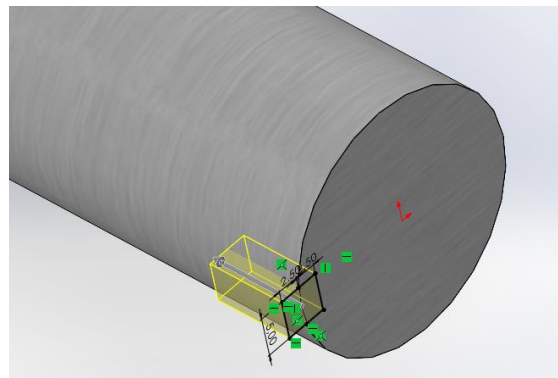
Segundo chavetero en el eje de la herramienta en SolidWorks.
